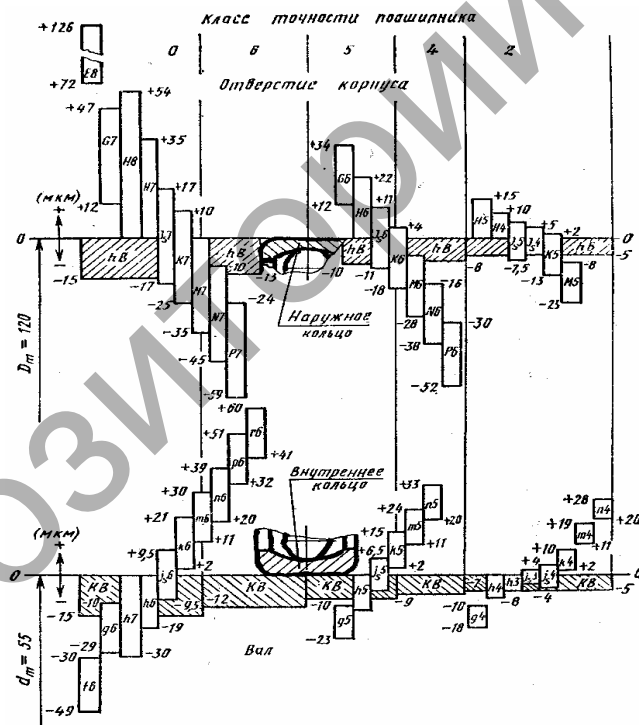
Схемы расположения полей допусков колец подшипников и сопрягаемых деталей
